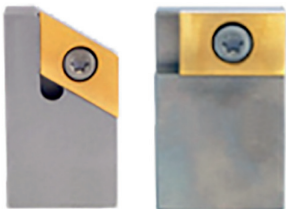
Держатели резцов для обработки фаски и торцовки
